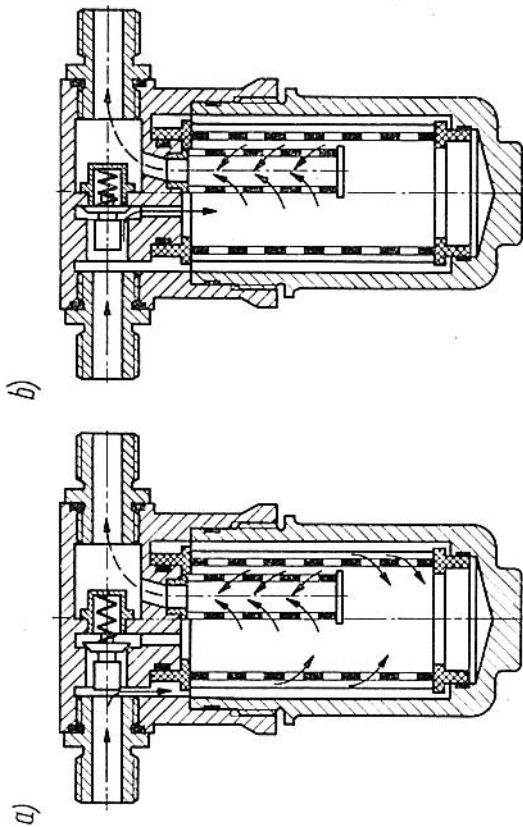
Sposób wbudowania i konstrukcja zaworów przelewowych filtru hydraulicznego
